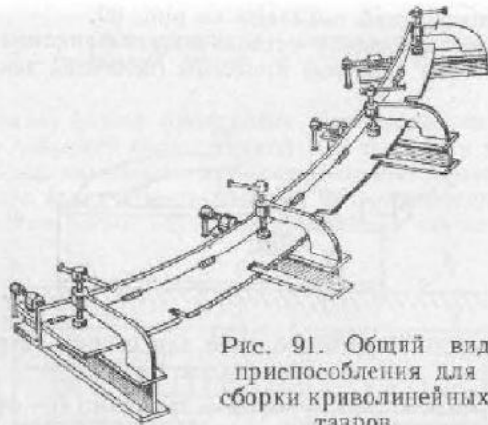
Общий вид приспособления для сборки криволинейных тавров.
